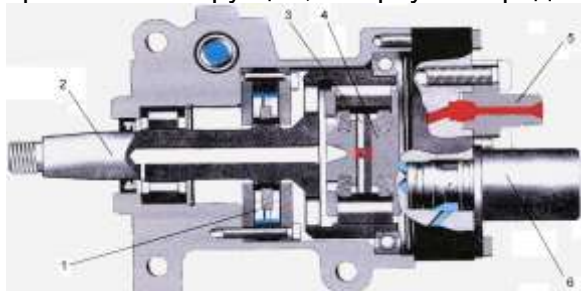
Внешний вид и разрез роторного ТНВД фирмы Delphi: 1 - ТПН; 2 - приводной вал с кулачковой шайбой; 3 - плунжер; 4 - ротор; 5 - напорный штуцер; 6 - регулятор расхода.
